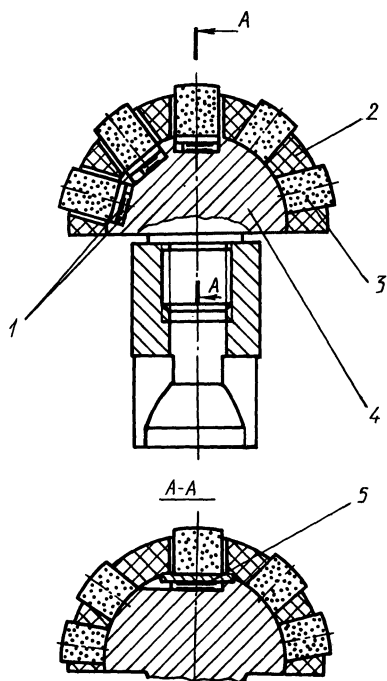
Сферический алмазный инструмент с датчиками давления: 1 — тензосопротивление; 2 — наполнитель; 3 — цилиндрические алмазные элементы; 4 — корпус инструмента; 5 — специальная упругая опора
